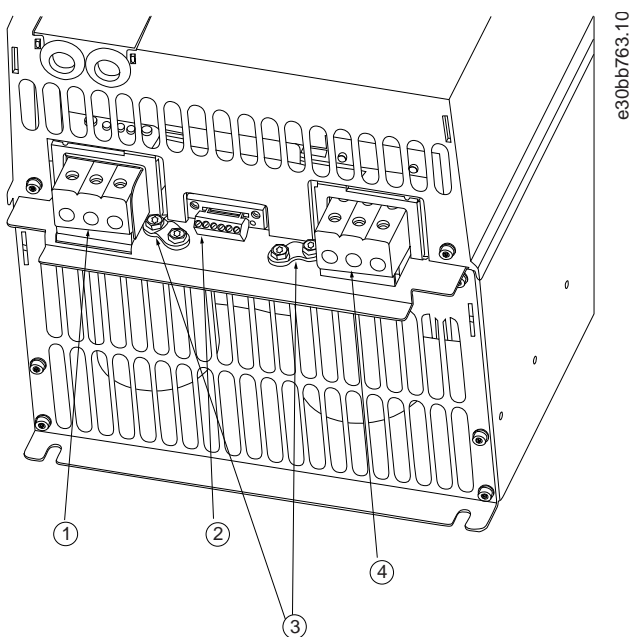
Baugröße H7 , IP20, 380–480 V, 55–75 kW (70–100 HP) , IP20, 200–240 V, 22–30 kW (30–40 HP) , IP20, 525–600 V, 45–55 kW (60–70 HP)
